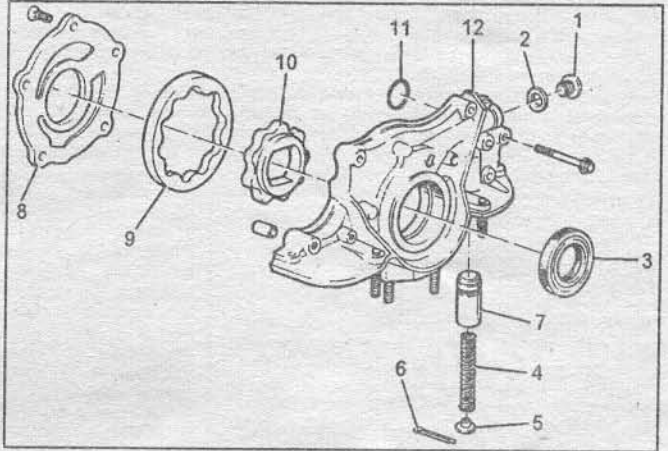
Сборка масляного насоса: 1 - заглушка; 2 - шайба; 3 - уплотнение; 4 - пружина; 5 - стакан; 6 - шплинт; 7 - редукционный клапан; 8 - крышка; 9 - внешний ротор; 10 - внутренний ротор; 11 - резиновое кольцо; 12 - корпус.
